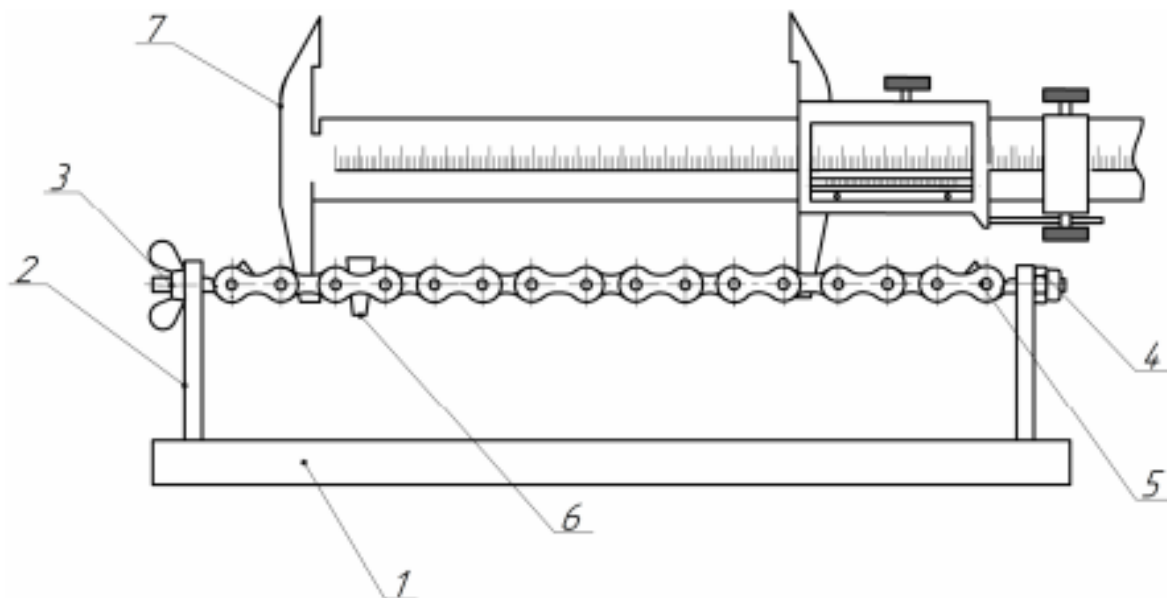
Схема установки: 1 – станина; 2 – стійка; 3 – рухомий фіксатор.; 4 – нерухомий фіксатор; 5 – ланцюг; 6 – клин; 7 – штангенциркуль
